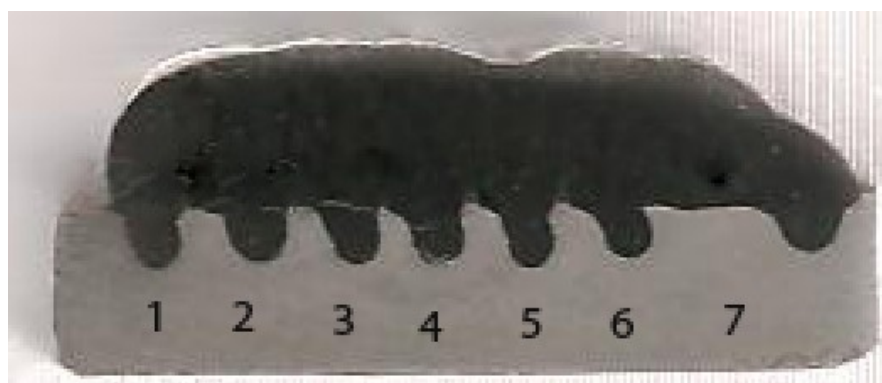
Macrografia da peça soldada pelo processo MIG, velocidade de soldagem de 30 cm/min.
